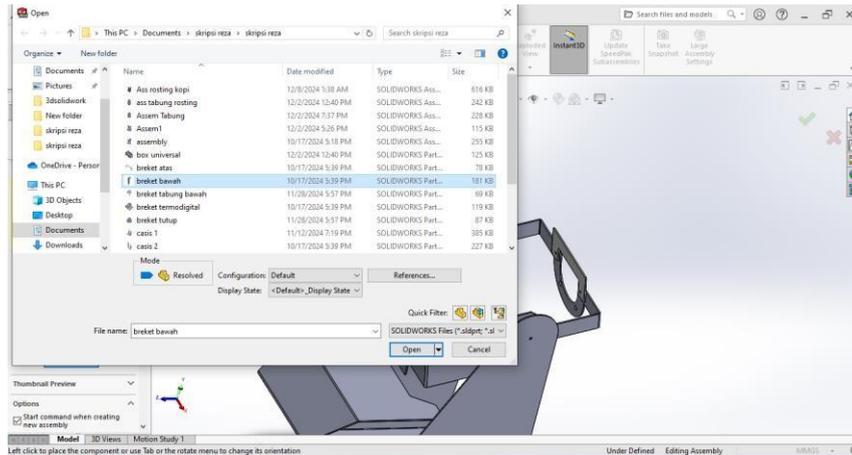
Assembly Part Bracket dan Chasis 2
